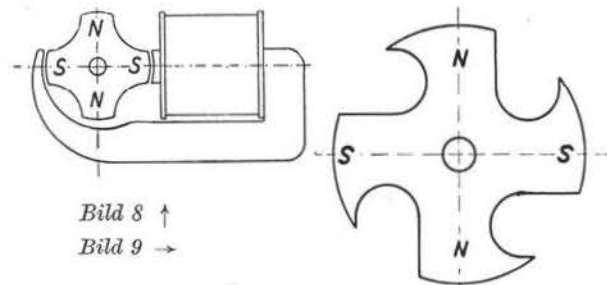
Synchronmotor mit Dauermagnetrotor für 1500 UpM bei 50 Hz.
